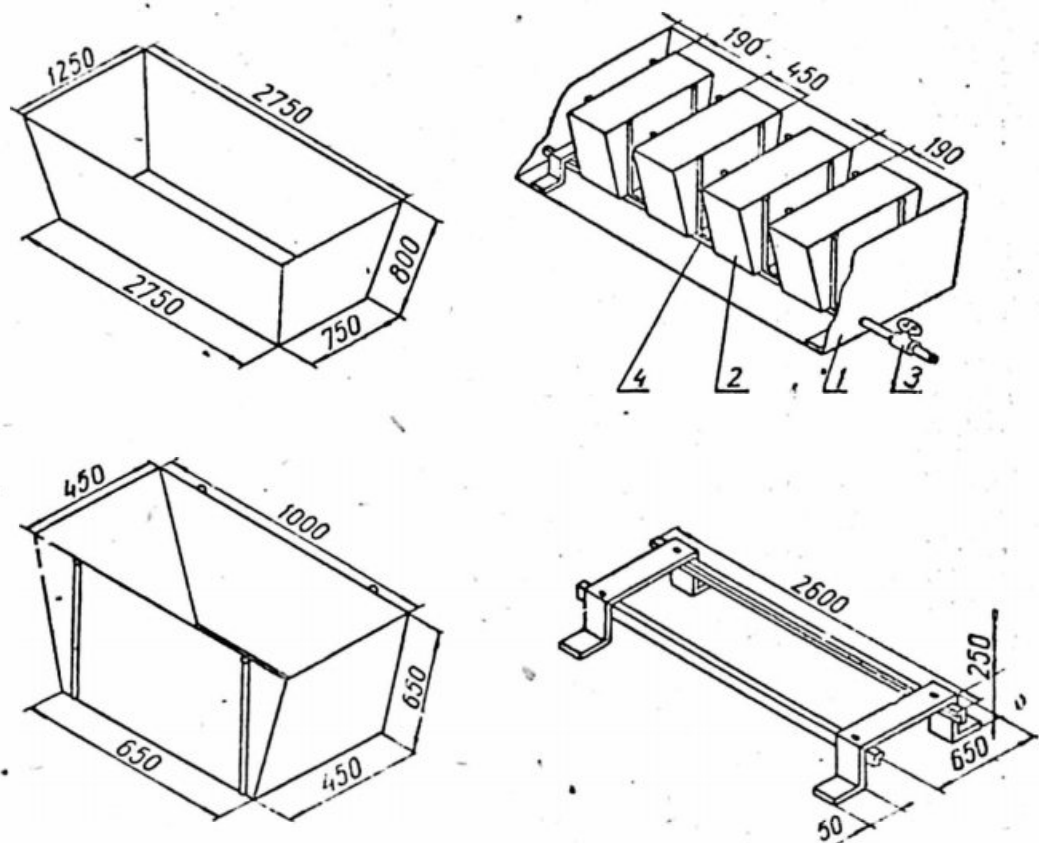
Справа: сверху — схема установки (1 — чан, 2 — вкладыш, 3 — сливной коан, 4 — подставка); внизу — вкладыш с подставкой. Слева: сверху — чан, внизу — вкладыш.
